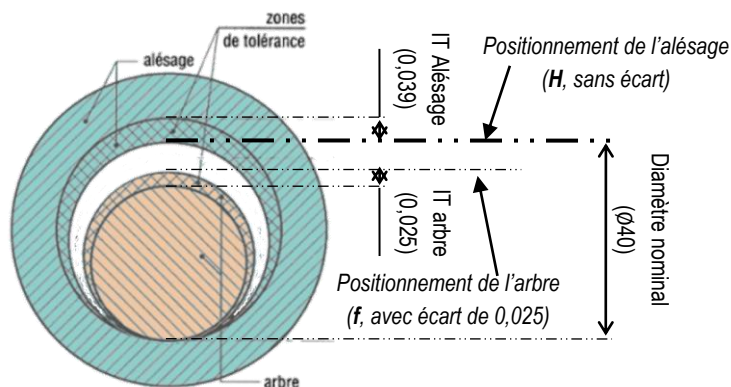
Ajustement $\varnothing 40H8f7$, vue axiale
